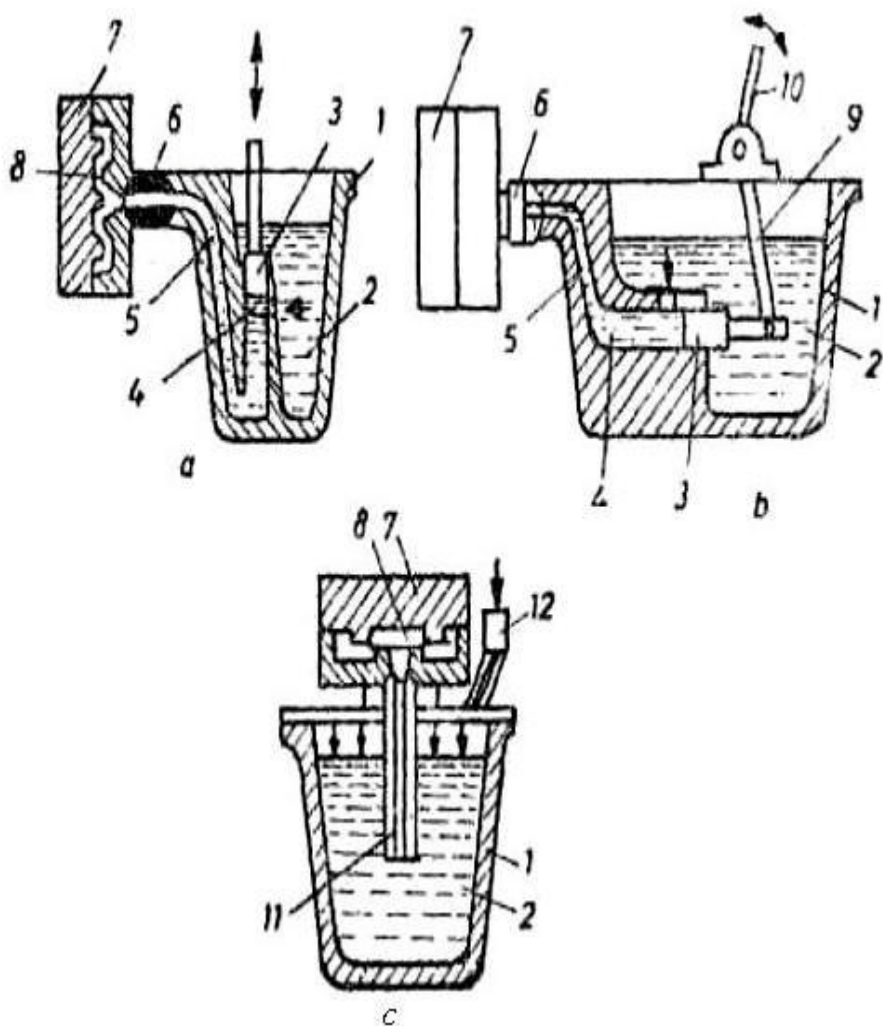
Mașini de turnare sub presiune cu cameră caldă de compresie cu piston vertical (a); cu piston orizontal (b); cu compresor cu baie închisă (c):
